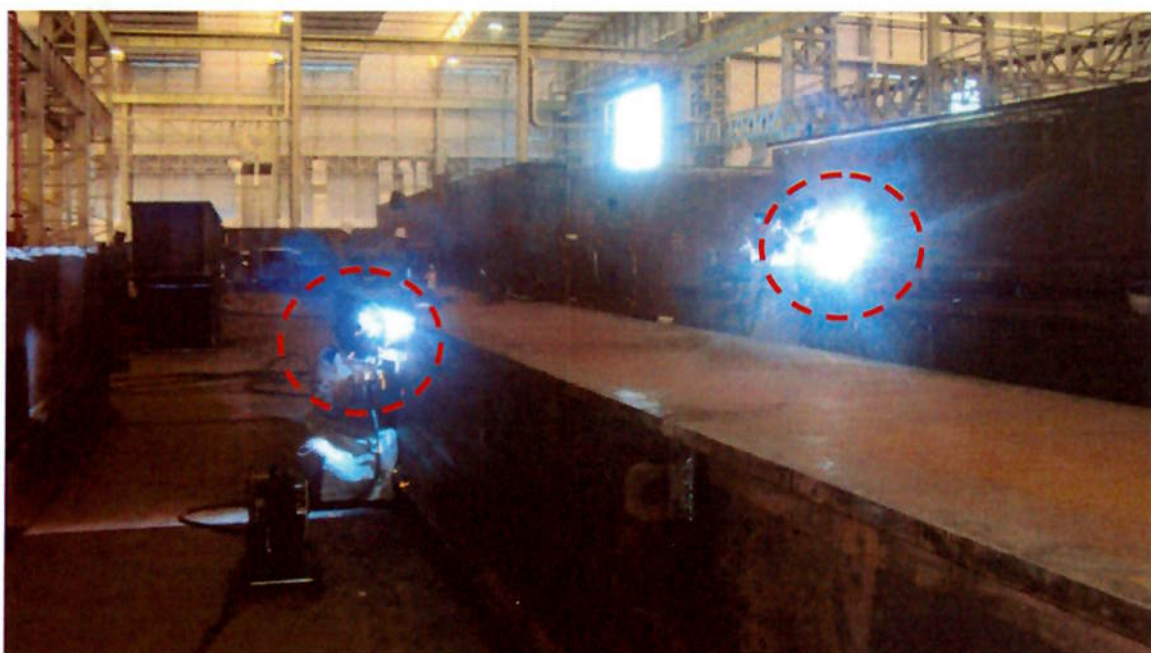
Exposição do soldador com radiação não-ionizante (local demarcado)
